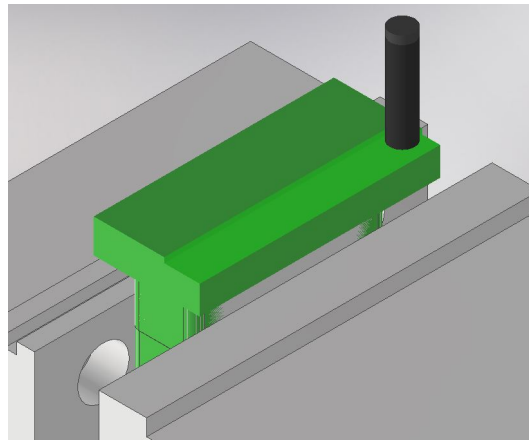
Montaje de stock resultante para segundo maquinado de punzón
